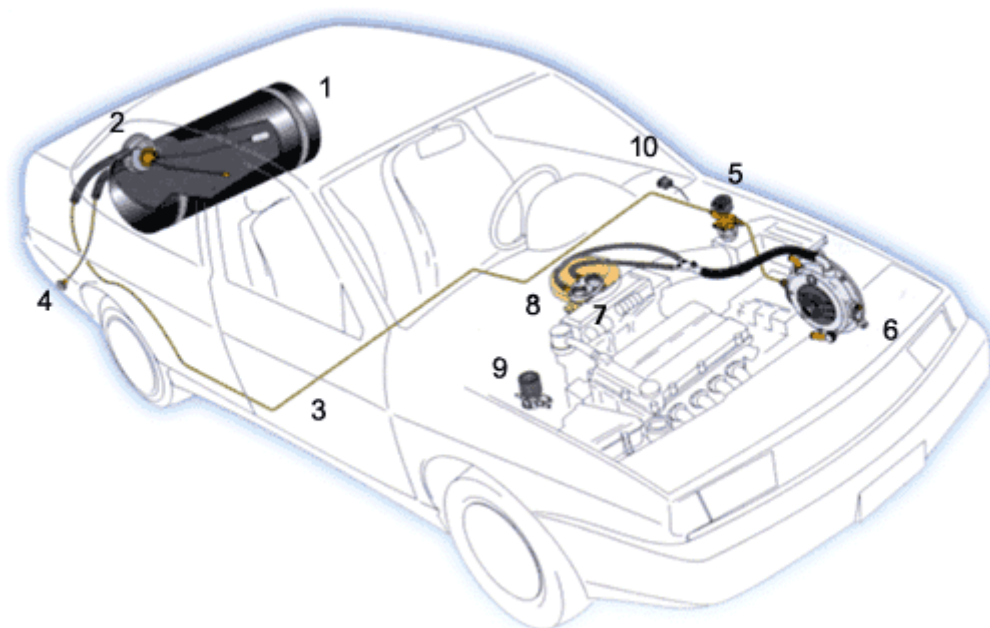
Схема установки газобаллонного оборудования: 1 – баллон с газом; 2 – мульти клапан; 3 – топливный трубопровод высокого давления; 4 – заправочное выносное приспособление; 5 – клапан для газа; 6 – редуктор-испаритель; 7 – дозатор топливной системы; 8 – клапан для бензина; 9 – топливный переключатель [22, с. 7].
